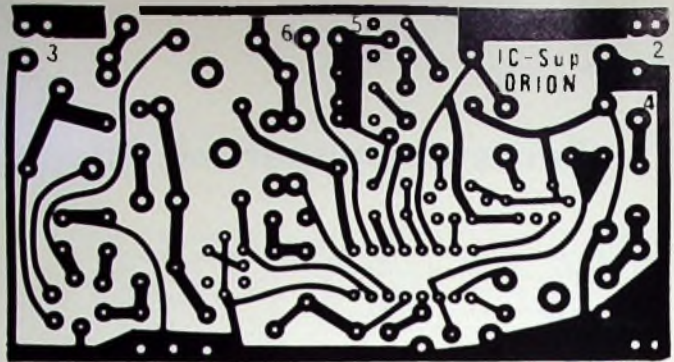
(oben) Printplatte für den Fernsteuersuper (Maßstab 1:1)
